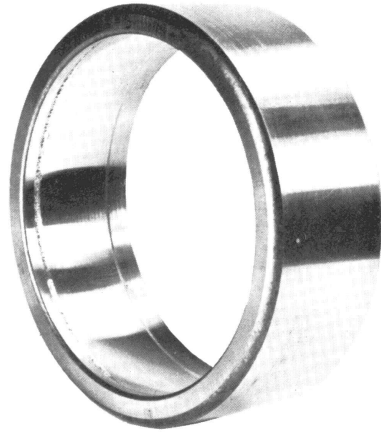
기생 스트레스에 의한 Spalling
